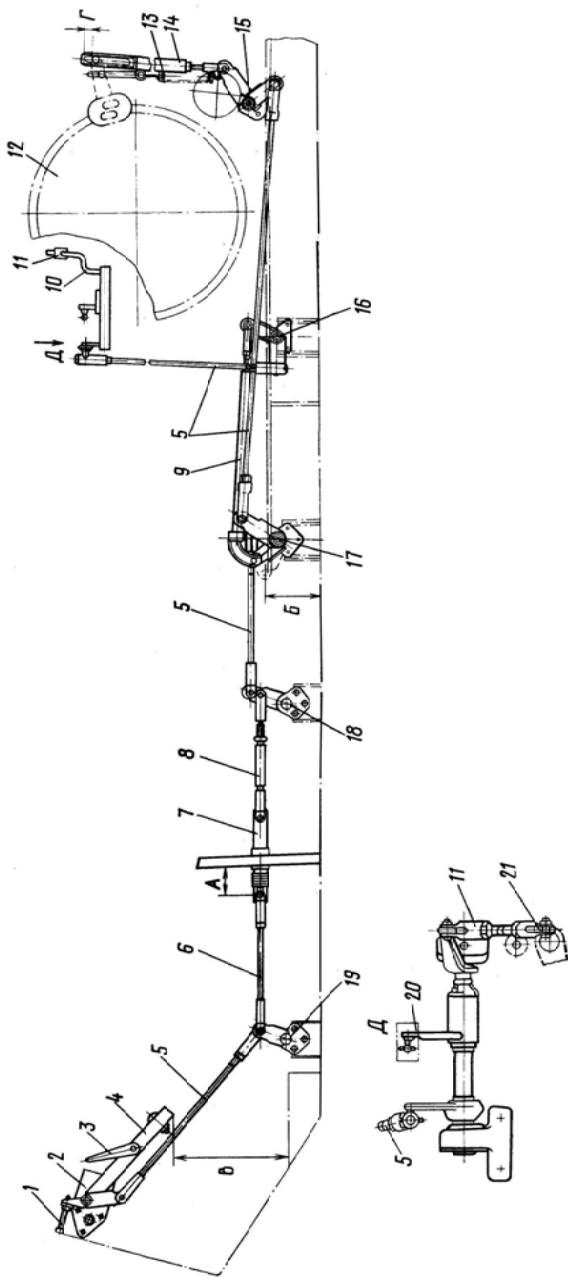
Привод управления остановочными тормозами ПМП:
